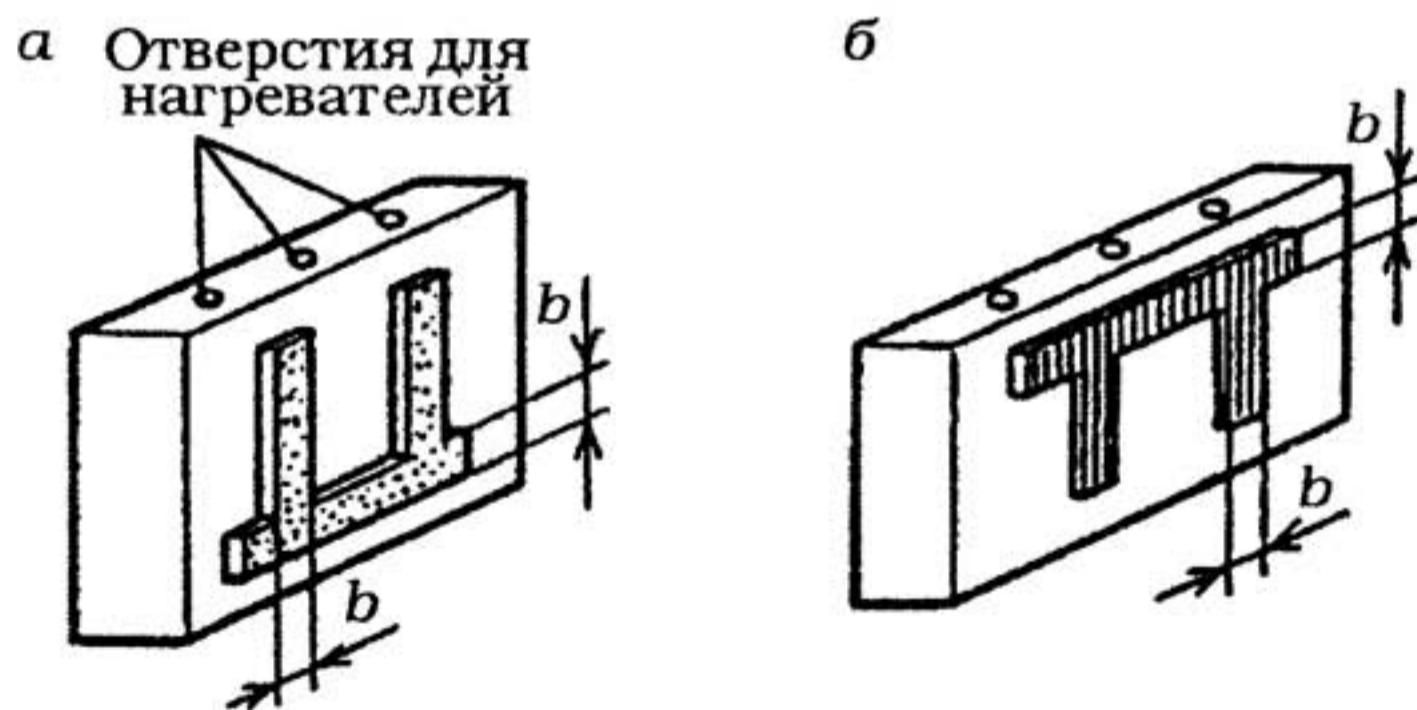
Плоские плиты для контактно-тепловой сварки с гладкой (а) и рифленой (б) поверхностями сварочного шва
